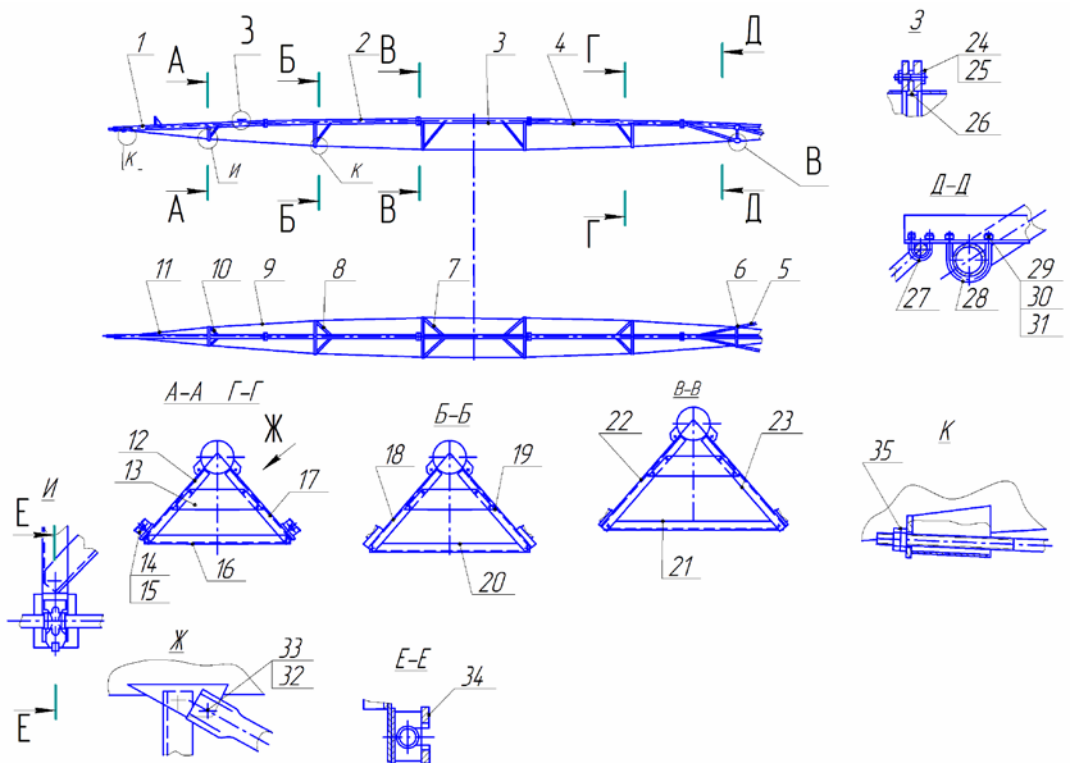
Ферма и консоль водопроводящего трубопровода машины
